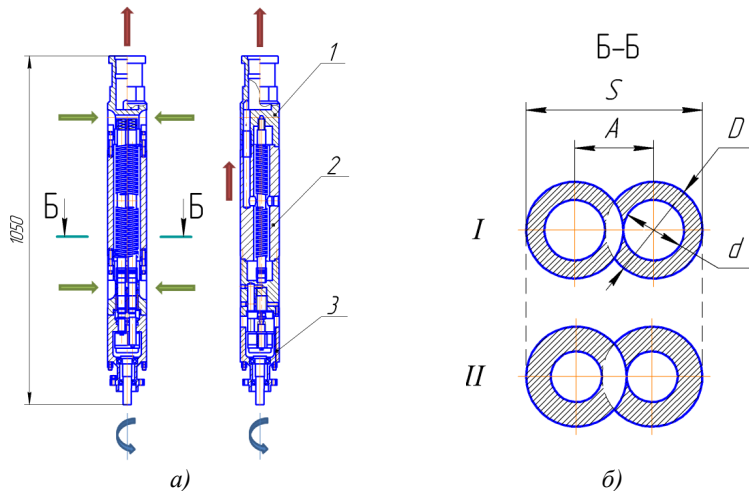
Скважинный двухвинтовой насос-компрессор марки НДПН-20/6:
